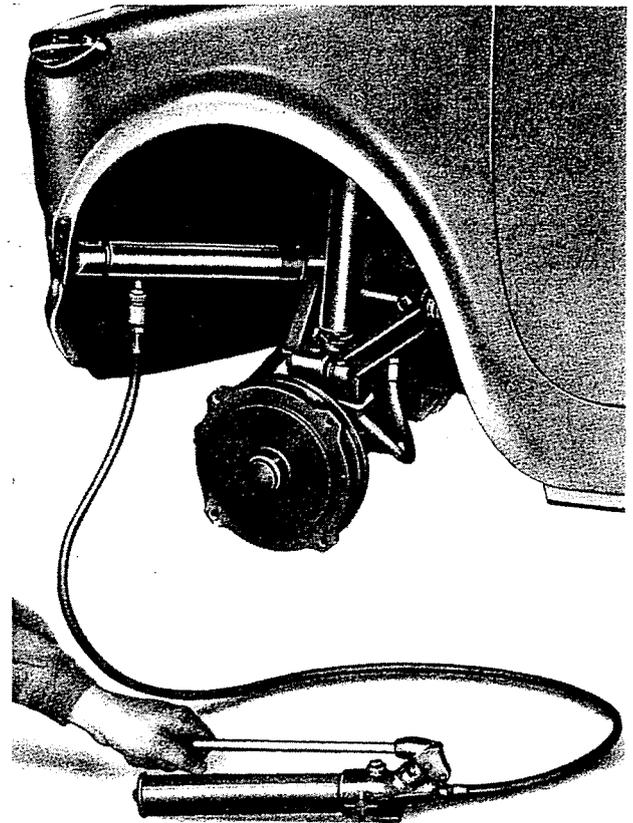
Anbringung des hydraulischen Druckzylinders am Wagen-Vorderteil.
